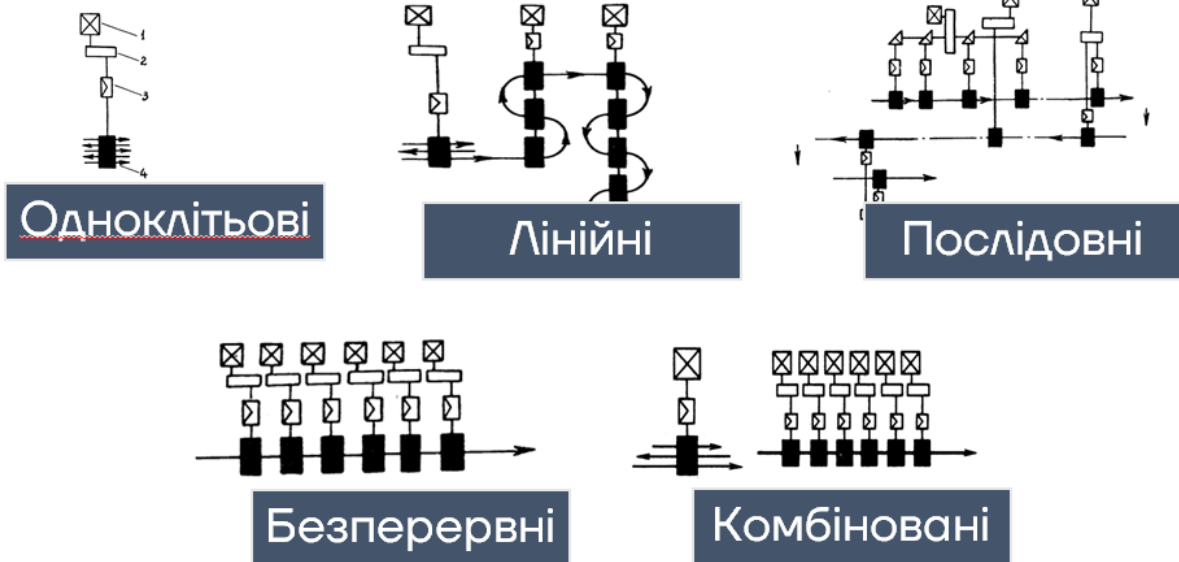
Схеми розташування робочих клітей та приводу багатоклітьових станів
